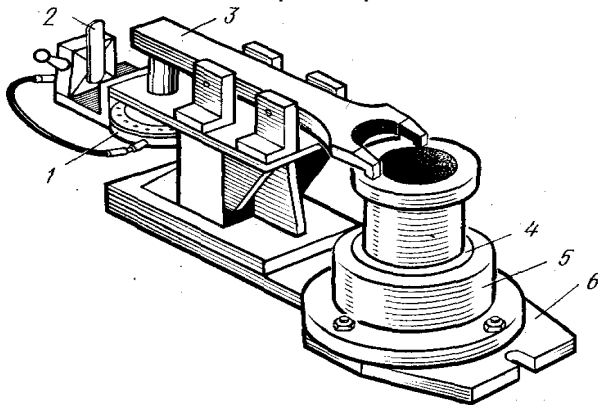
Приспособление для установки и крепления гильз: 1 — пневматический привод; 2 — кран управления; 3 — прижим; 4 — центрирующее кольцо; 5 — корпус; 6 — основание
